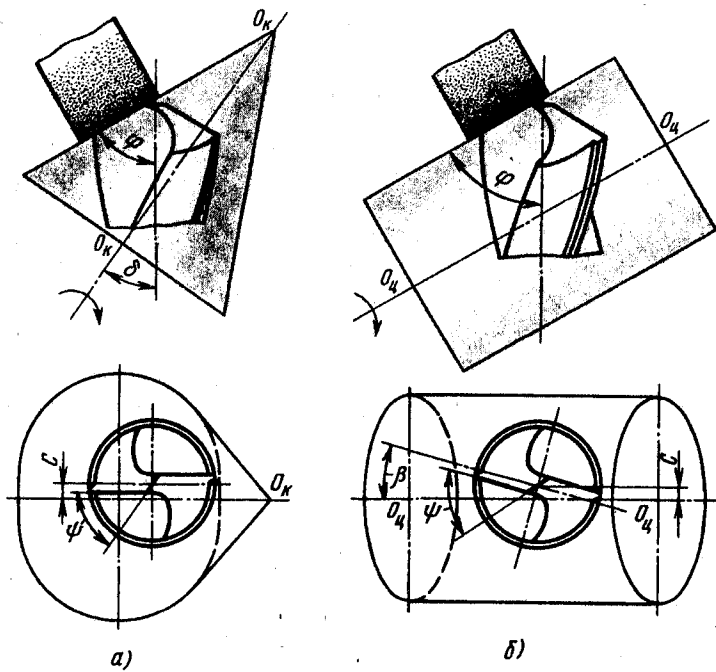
Заточка спирального сверла с конической (а) и цилиндрической (б) задней поверхностью
